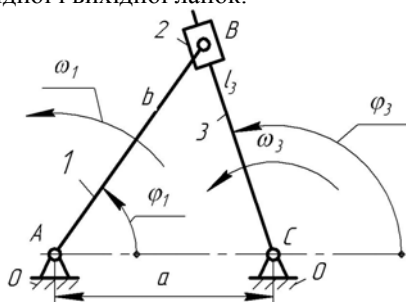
Центральний двокривошипний кулісний механізм ($a = \text{const}$)
